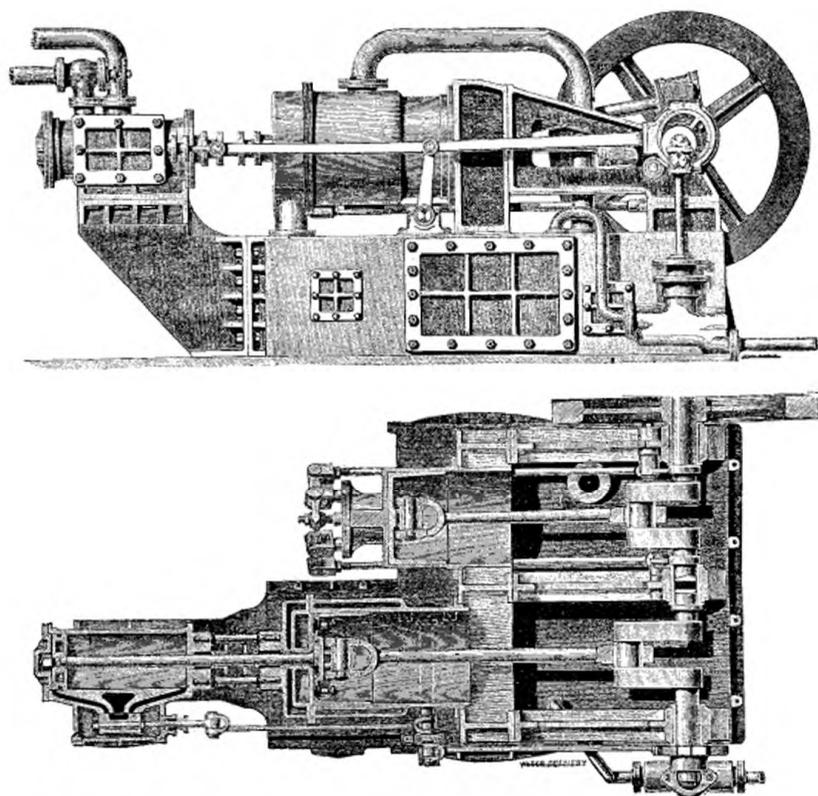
et 26. — *Giffard*, Machine horizontale de 600 mètres cubes,
